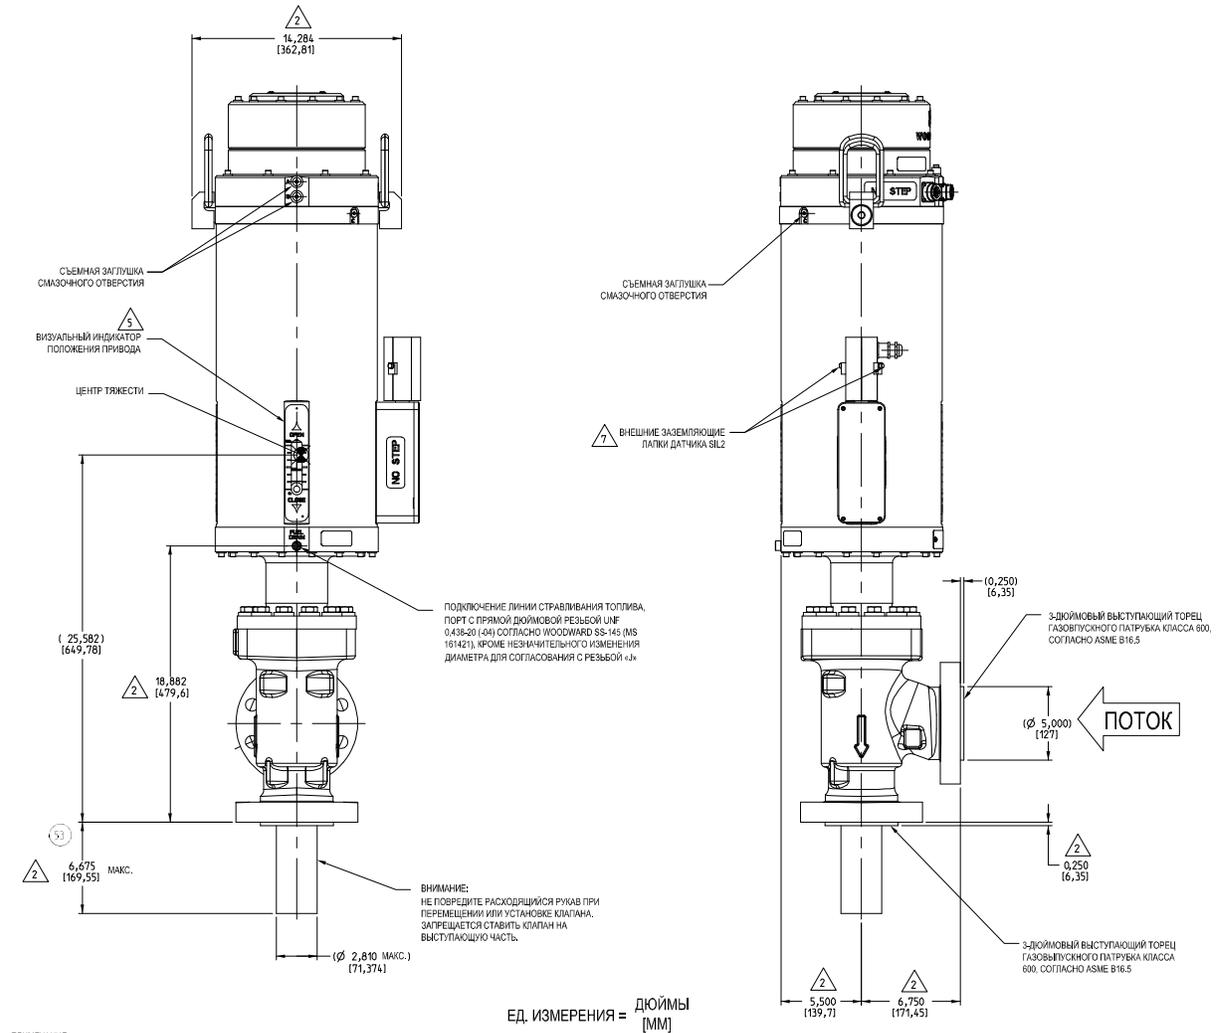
Габаритный чертеж (2-дюймовый клапан LESV II со сверхвысоким коэффициентом восстановления, нержавеющая сталь, двойной резольвер класса 600#)
